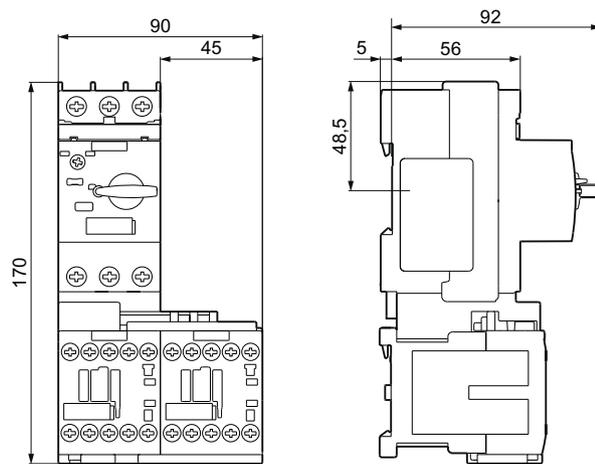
Arrancador inversor S00, AC/DC, bornes de tornillo 3RA2210-..A
